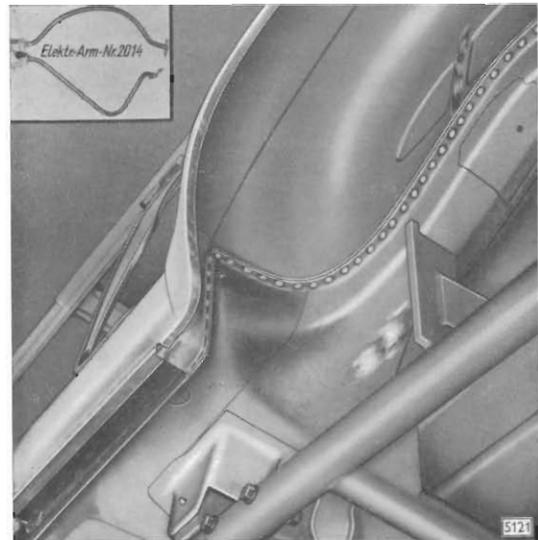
Radeinbau an Bodenblech zangenpunktgeschweißt
